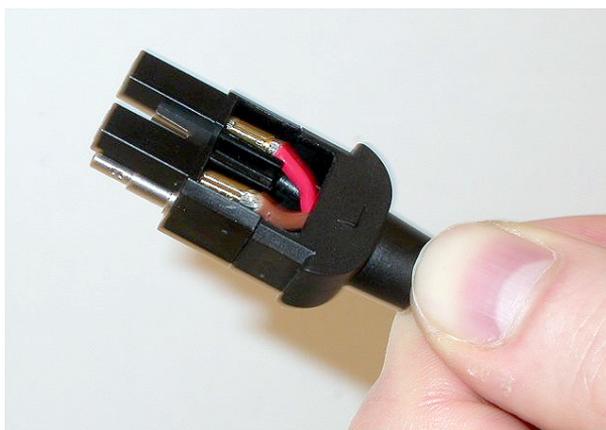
Assemblaggio del blocco di montaggio/involucro posteriore
